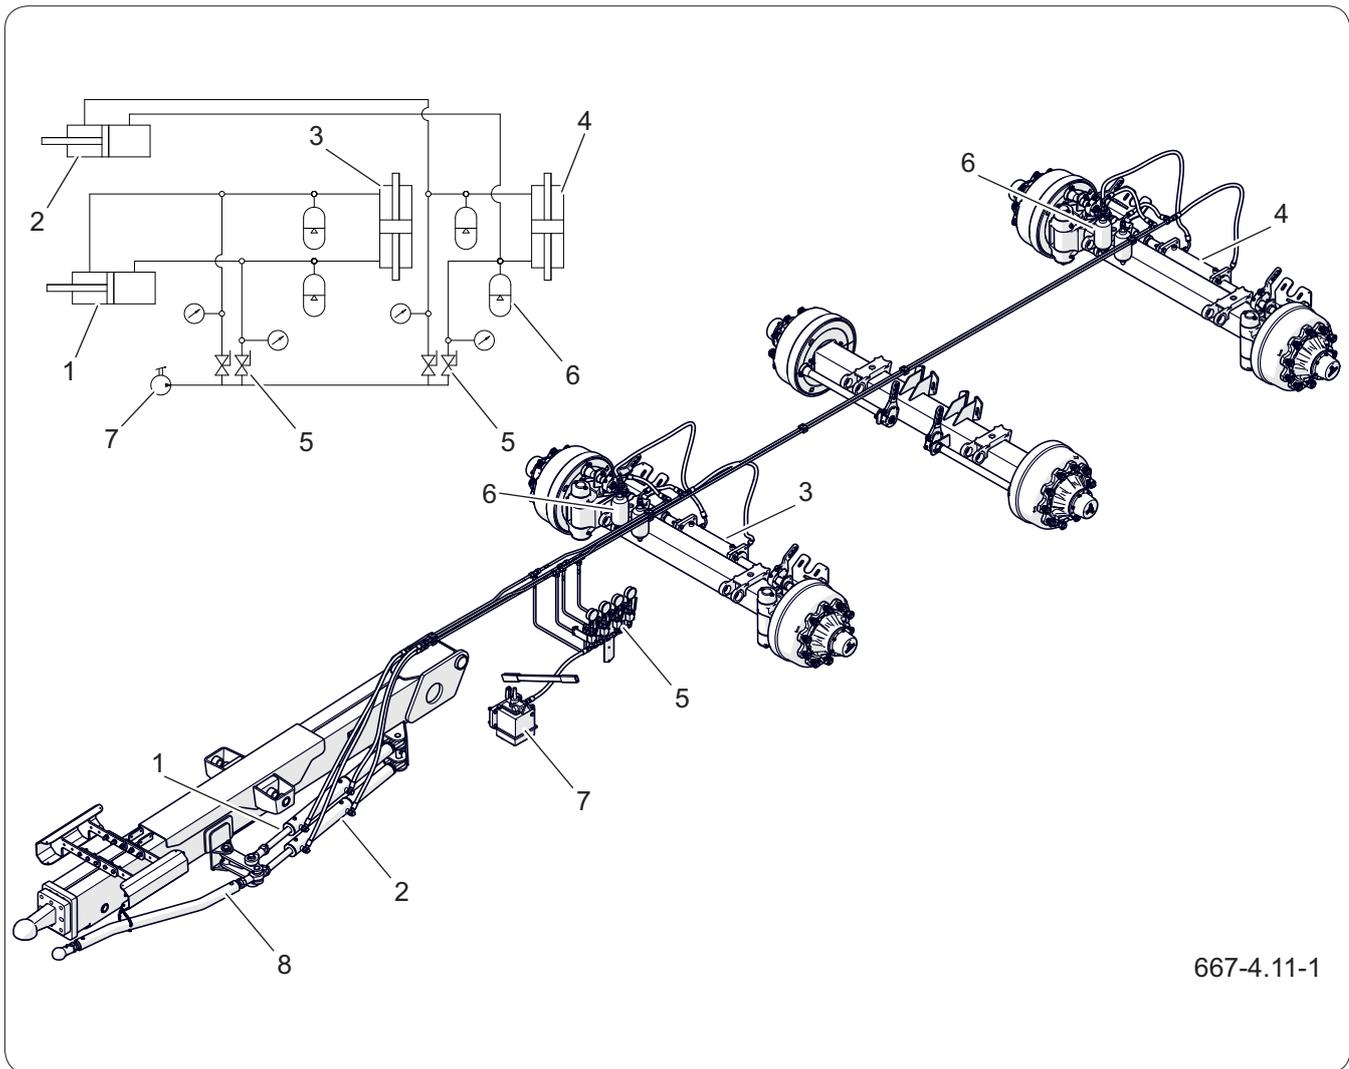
Construction et schéma de l'installation hydraulique du timon
